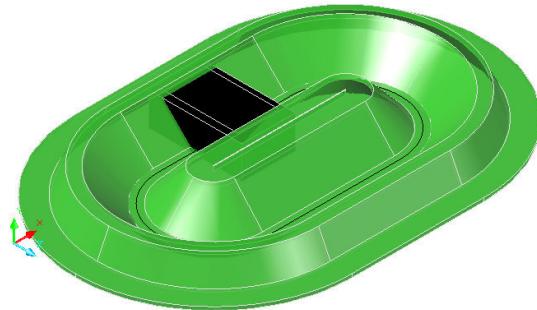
Компонування камери розташування аераторів і корпусу ЦОК
